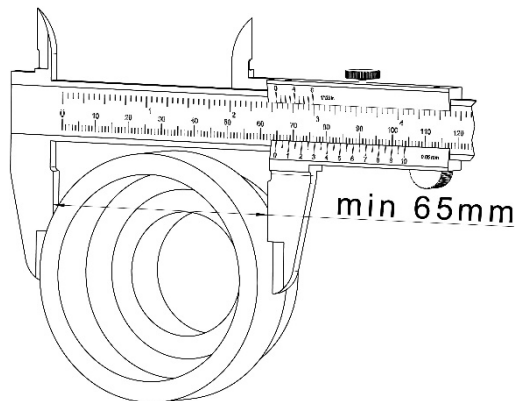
Zulässiger Verschleiß an Kolbenführung
